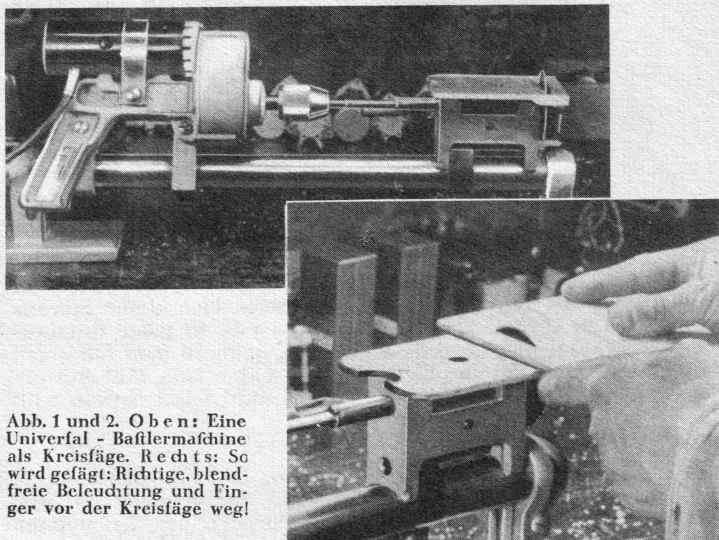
und 2. Oben: Eine Universal - Bastlermaschine als Kreisläge. Rechts: So wird gefügt: Richtige, blendfreie Beleuchtung und Finger vor der Kreisläge weg!
